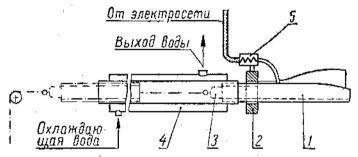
Приспособление для изготовления сварных труб из термопластов.
